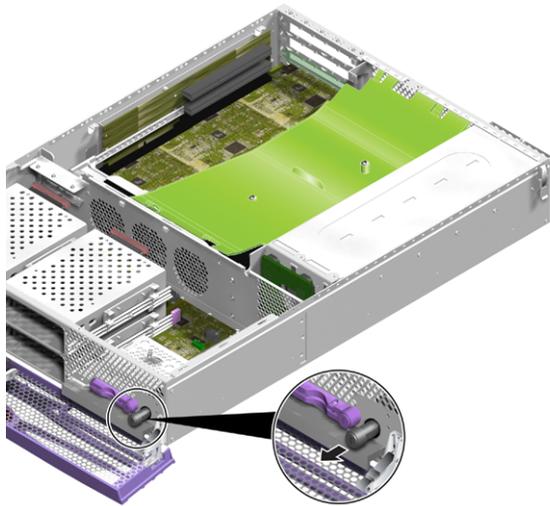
Desconexión del arnés de cables de la cerradura de contactos
